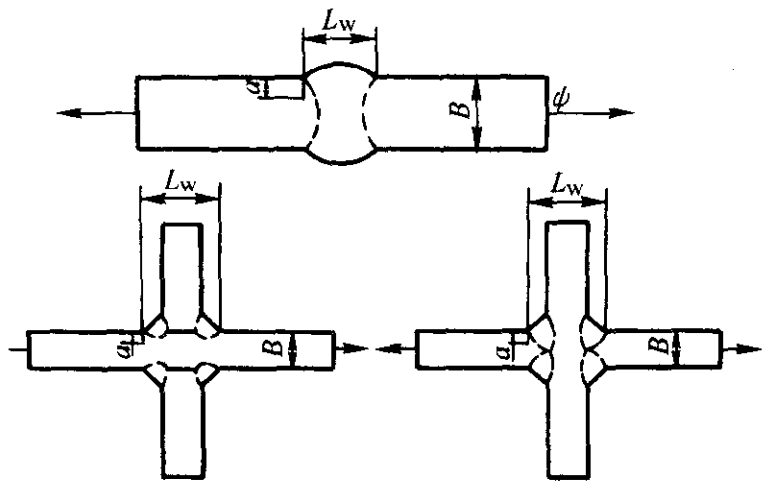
焊趾处表面裂纹的结构尺寸
